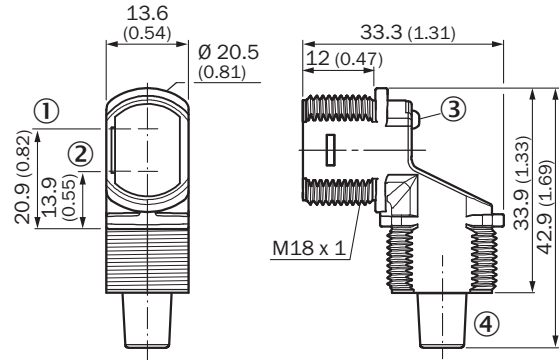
ZLx18-4xxxxx/ZLx18-Dxxxxx, cable
